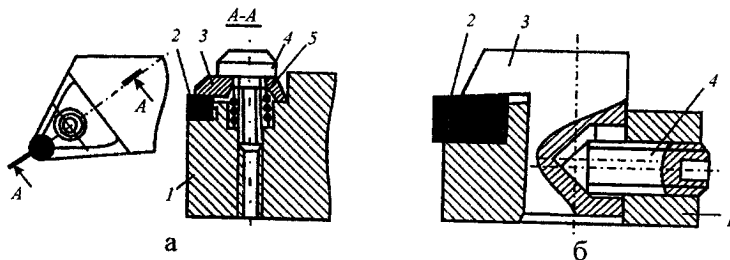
Різці з механічним кріпленням пластин із НТМ: кріплення пластини прихватом зверху (а) і гвинтом збоку (б): 1 – корпус; 2 – пластина; 3 – прихват; 4 – гвинт; 5 – пружина
